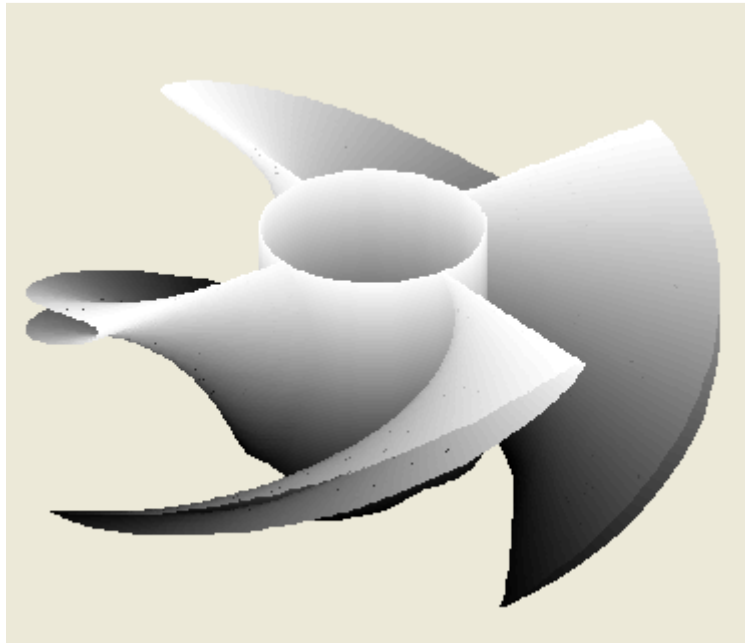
Geometría tridimensional del Rotor de la Turbina Axial calculada
